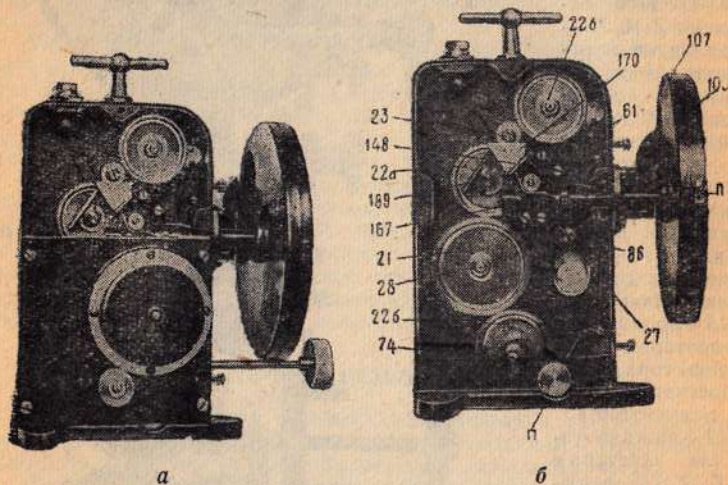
Внутренний вид передаточного механизма головки: а — с одной снятой крышкой корпуса, б — с двумя снятыми крышками корпуса
